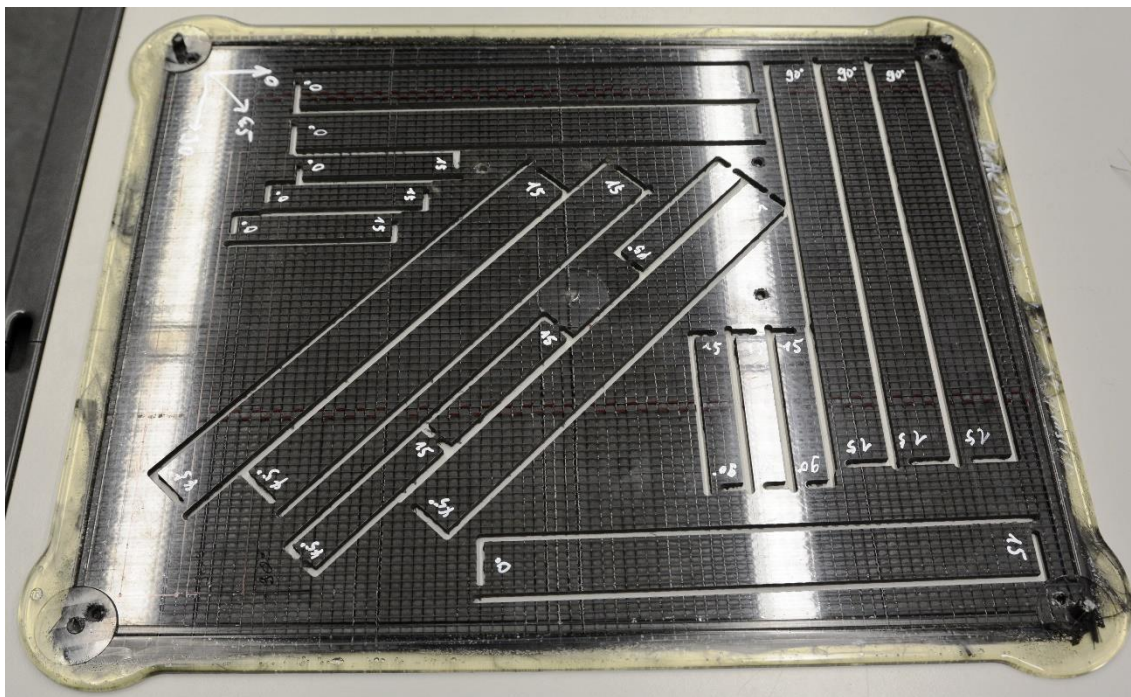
Versuchsplatte mit ausgefrästen Prüfkörpern
